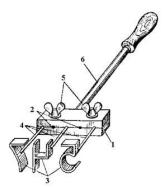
Приспособление для таврирования рыбы. 1 - резная державка; 2 - отверстия для матриц; 3 - матрицы; 4 - винты с барашками; 5 – рукоятка
